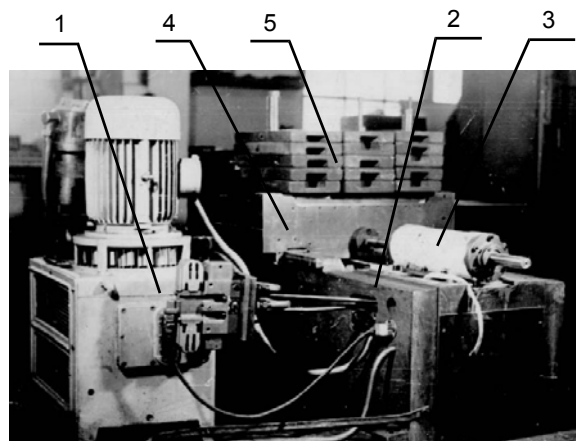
Стенд для дослідження напрямних фрезерних верстатів: 1 – гідростанція; 2 – досліджувана станина; 3 – гідро циліндр переміщення стола верстата; 4 – стіл верстата; 5 – вантаж, який імітує навантаження стола верстата.
